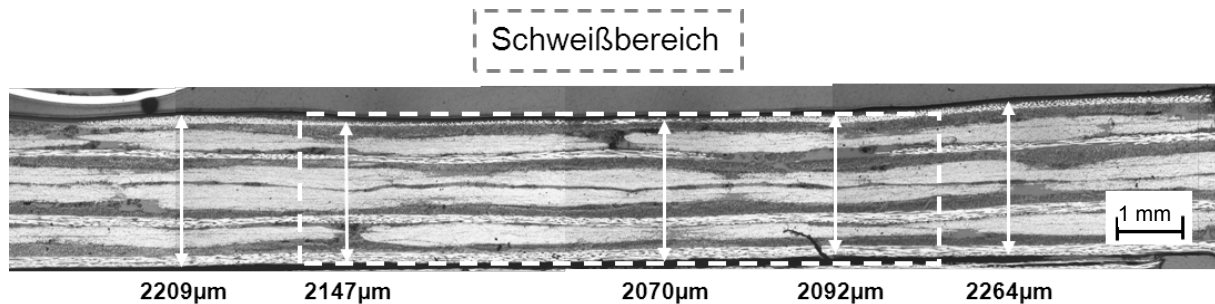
Schliffbild bei Schnitt quer durch eine Schweißnaht im ausgehärteten Laminat (VARI-Verfahren), Probe 1
